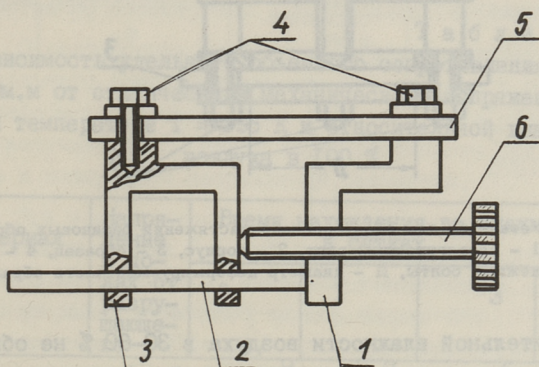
Установка для одностороннего растяжения резиновых образцов: 1 - корпус, 2 - направляющие салазки, 3 - каретка, 4 - крепежные болты, 5 - образец, 6 - растягивающий винт.
